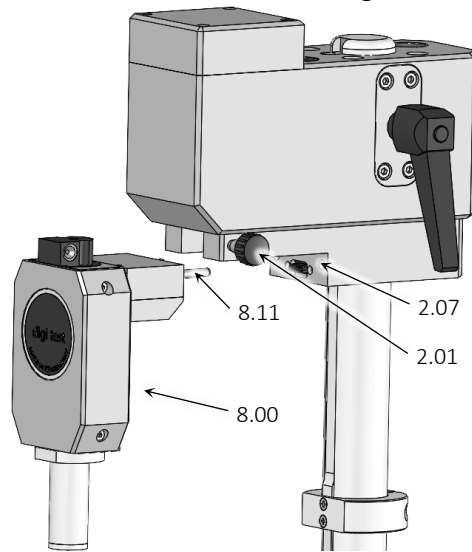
Befestigung der Messeinrichtung am Aufnahmearm
